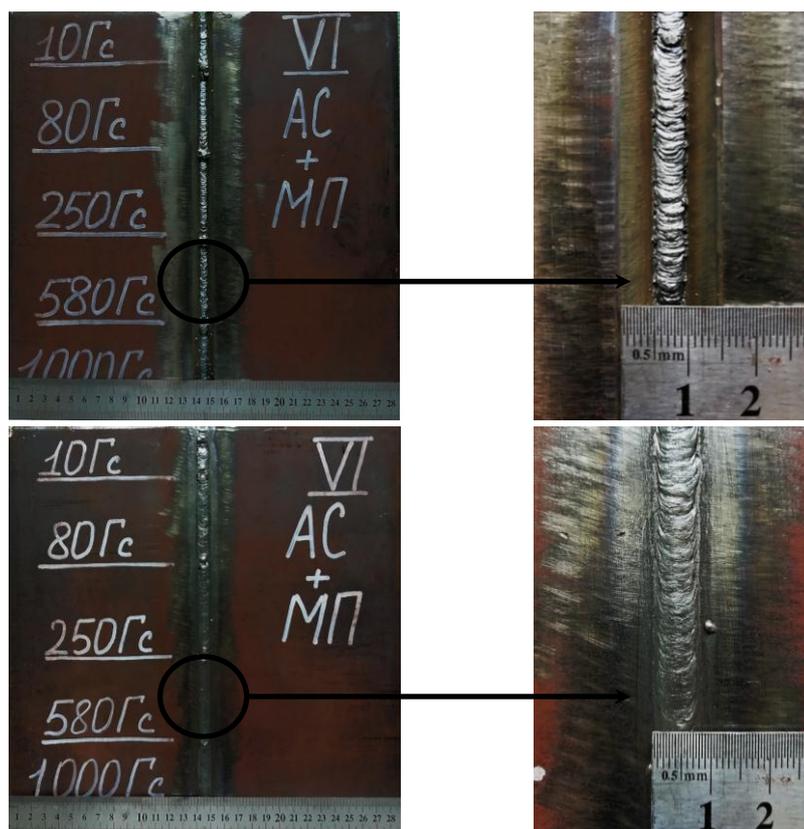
Лицевая сторона и обратный валик сварного соединения, выполненного на переменном прямоугольном токе во внешнем магнитном поле
